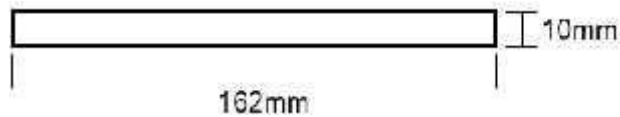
Pieza de Chasis a calcular. Vista Izquierda
